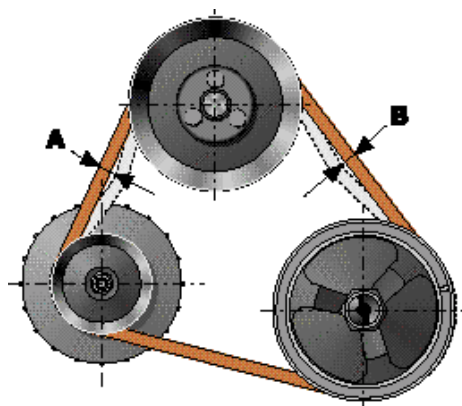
Схема проверки натяжения ремня привода генератора и жидкостного насоса двигателя мод. 2106-70
